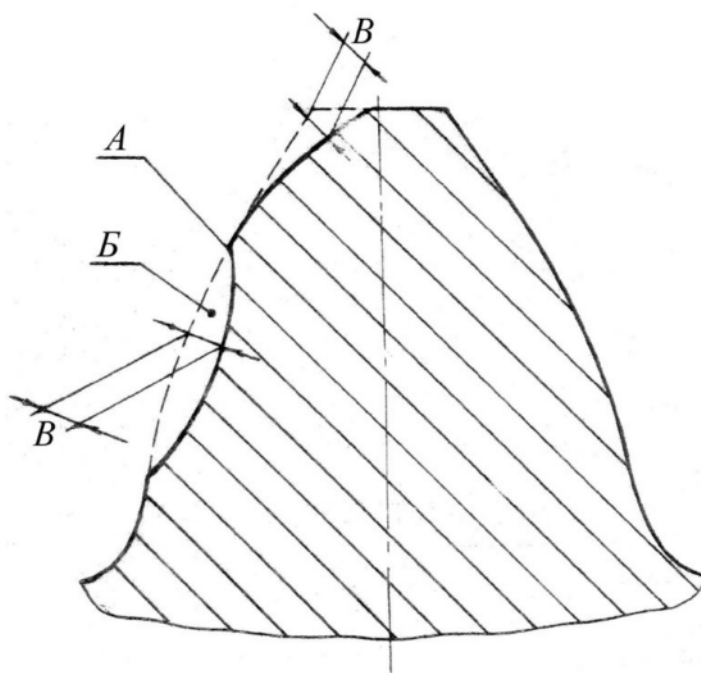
Схема износа рабочего профиля зуба зубчатого колеса: А — "хребет" в полюсе зацепления; Б — поднутрение; В — износ.
